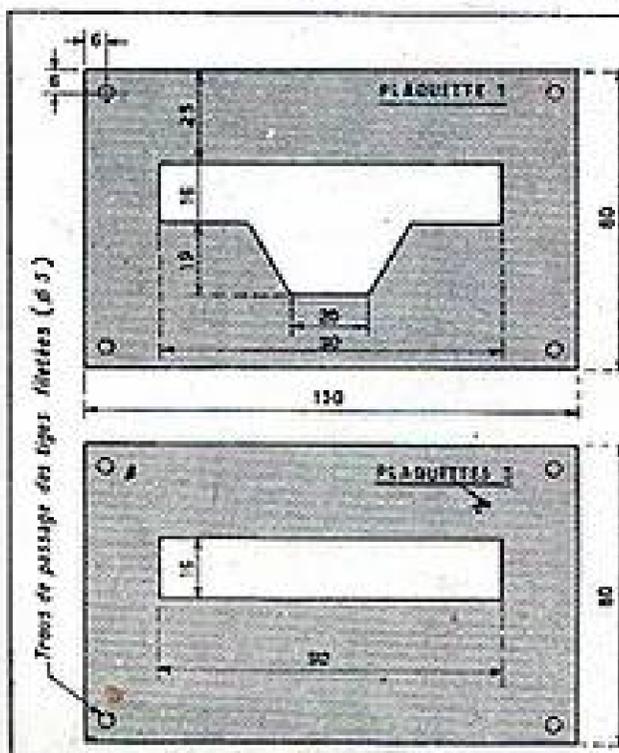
LA PLAQUETTE 2 de même dimension reste plane
